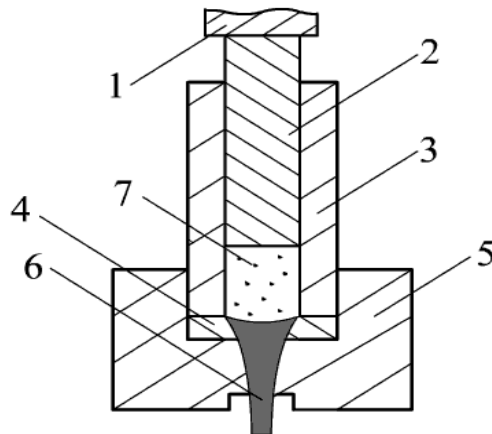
Схема мундштукового пресування: 1 – плунжер преса; 2 – пуансон; 3 – сталевий циліндр; 4 – конус; 5 – матриця; 6 – пресована заготовка; 7 – порошок
